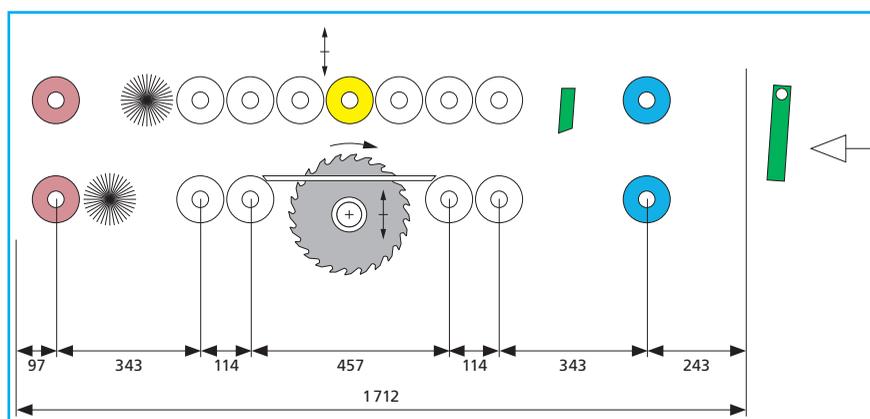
Walzenausstattung einer M34 mit Vollausrüstung
